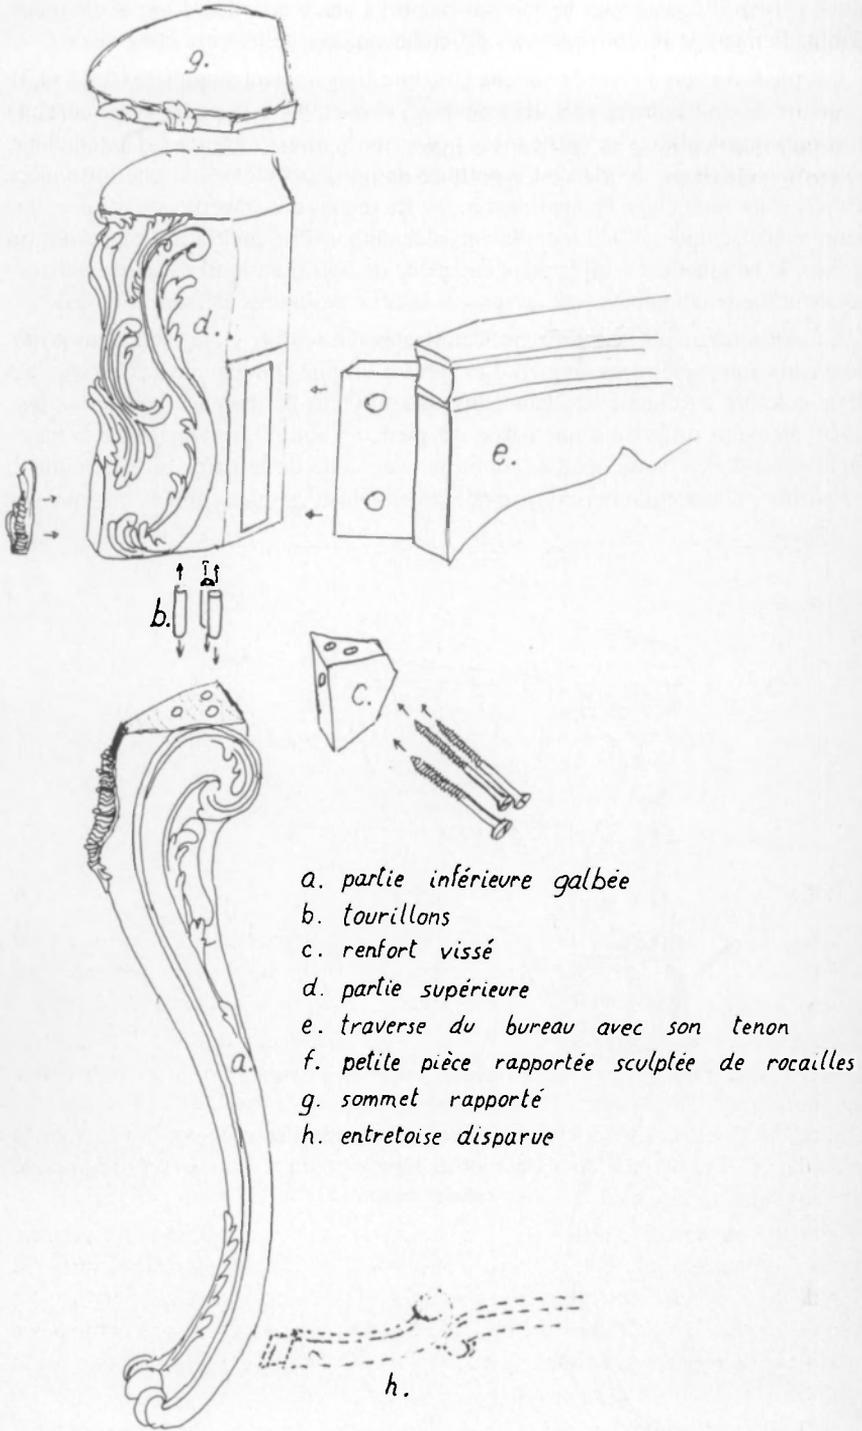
Vue éclatée d'un pied du bureau (dessin P.B.).
